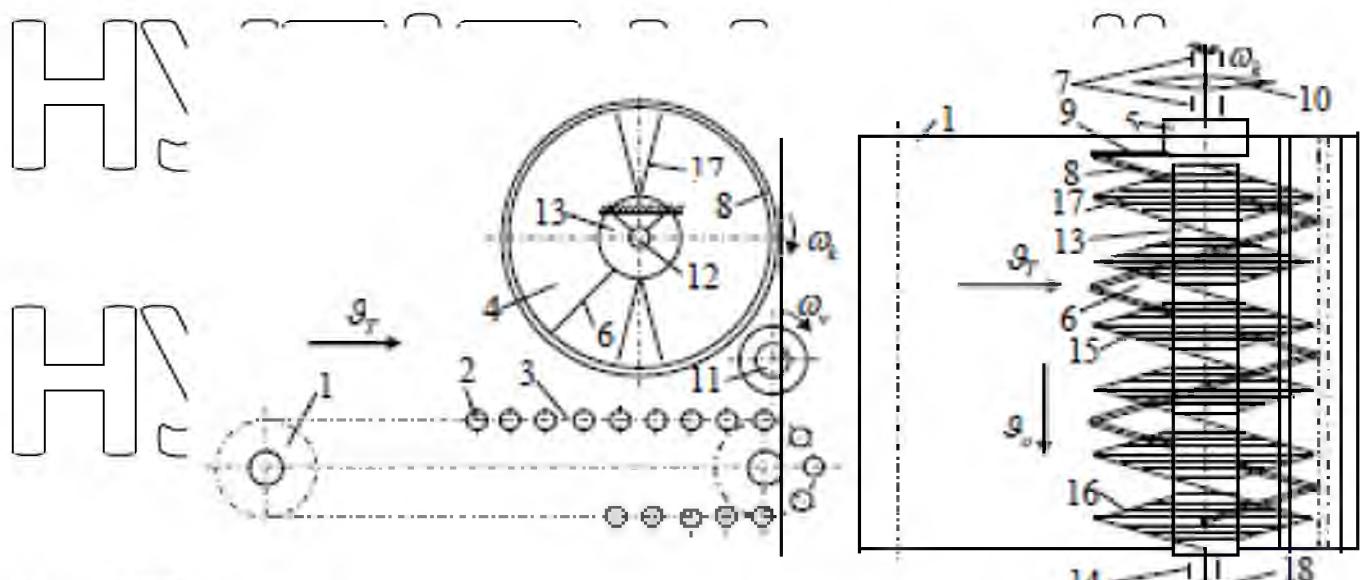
Конструктивна схема очисника вороху: 1 – подавальний транспортер; 2 – пруток; 3 – робоча гілка; 4 – комбінований робочий орган; 5 – пустотілий гвинтовий циліндр; 6 – виток; 7, 14 – опора; 8 – труба; 9 – фланець; 10, 18 – зірочка; 11 – відкидний валець; 12 – пригодний вал; 13 – барабан; 15, 16 – гвинтова лінія; 17 – очисні елементи.
